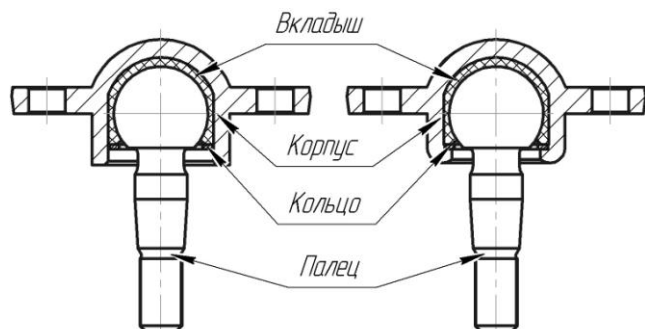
Шаровой шарнир с соединением КН до и после сборки
